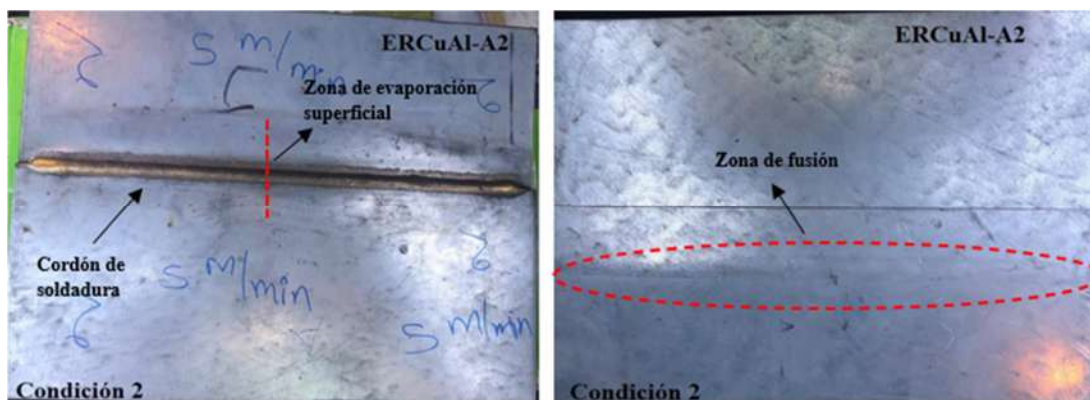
Unión soldadas con el electrodo ERCuAl-A2 mediante el proceso GMAW-P Brazing. C2-B.
